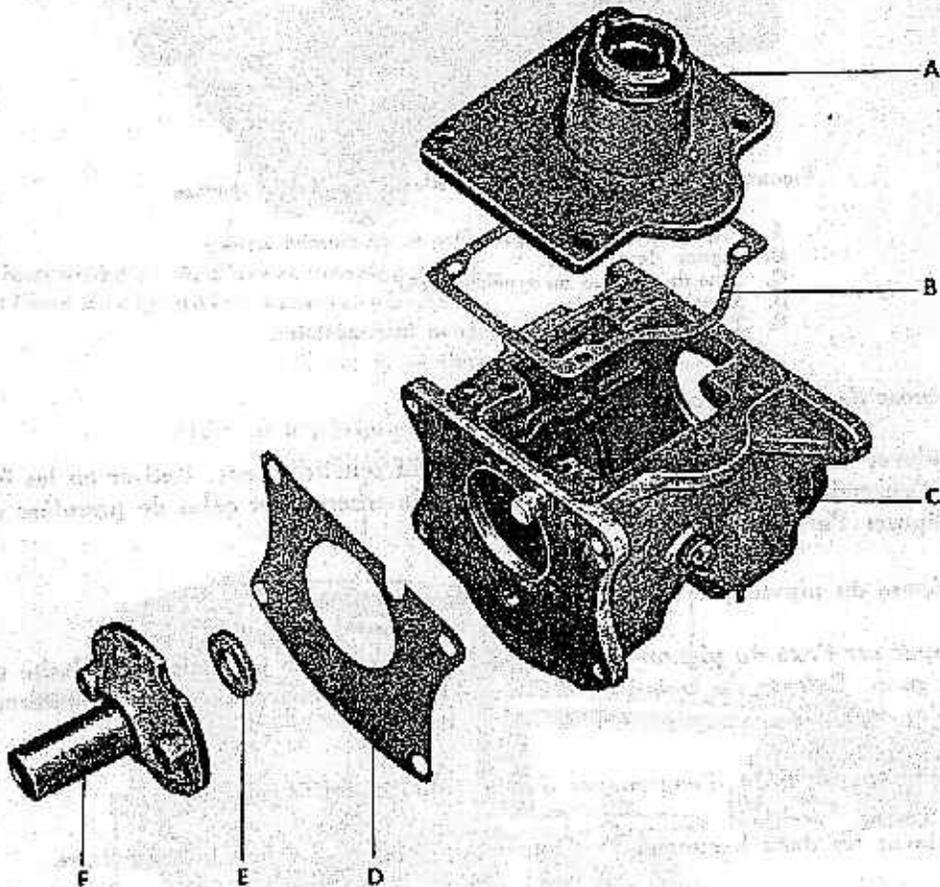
Carter de boîte de vitesses et ses couvercles. Vue éclatée
